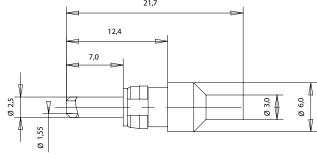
Zeichnung LWL-Steckverbinder Buchse
